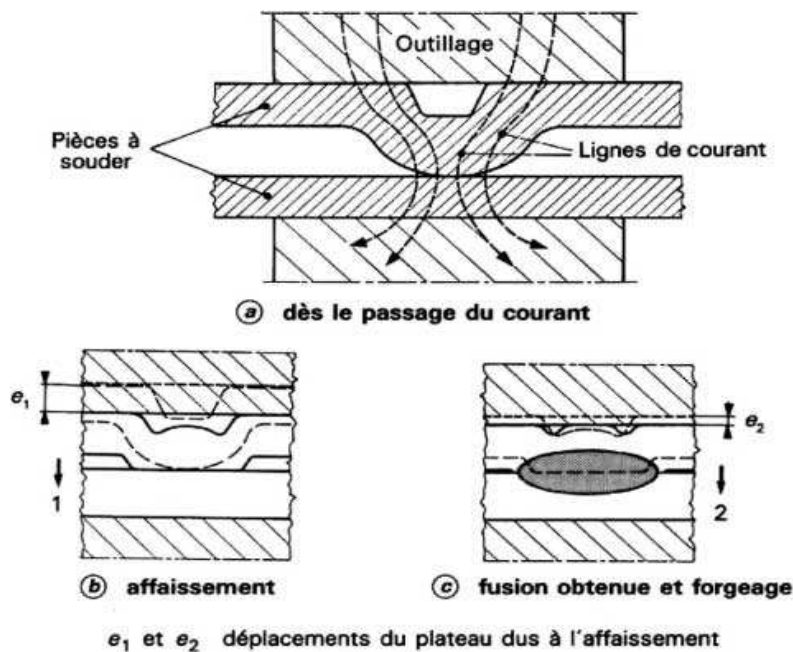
Soudage par bossages, formation de la soudure.
